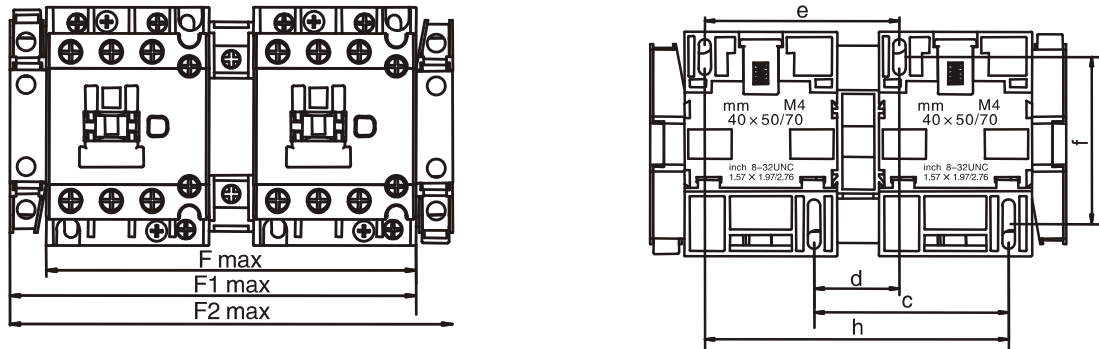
Габаритные и установочные размеры контакторов с реверсивной сборкой на токи 9-38А, мм.
